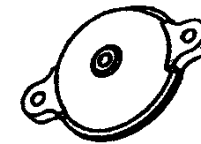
Крышка подшипника КИР.23.0.1011
